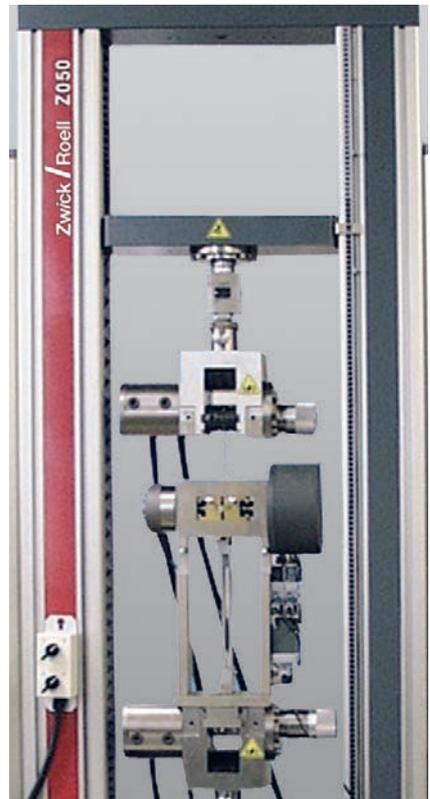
Material-Prfmaschine Z050 mit Draw-Bead Werkzeug
